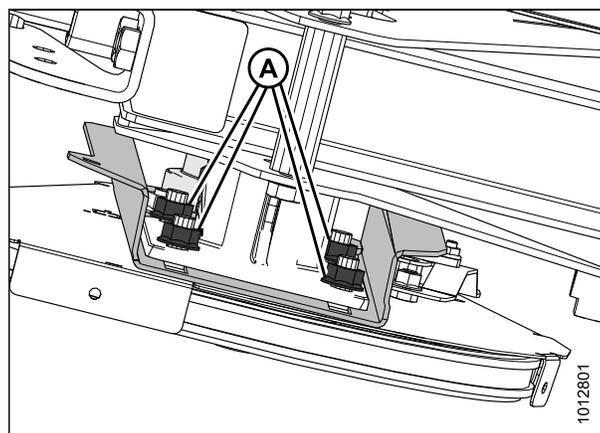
Привод единого мотовила — вид со стороны нижней части подбирающего мотовила
